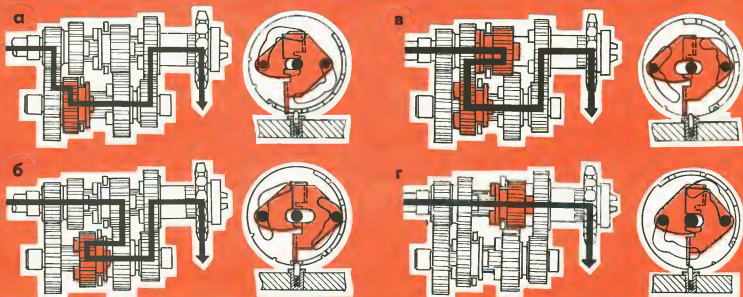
Схема положения шестерен коробки и механизма переключения (справа) при включении передач: а — первой; б — второй; в — третьей; г — четвертой.
